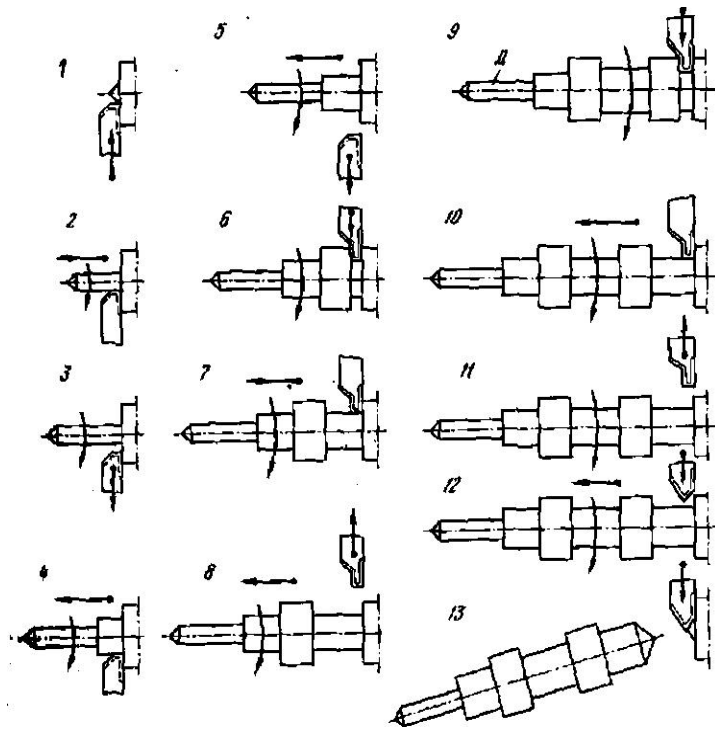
Схеми обробки заготовок на автоматі поздовжнього точіння
